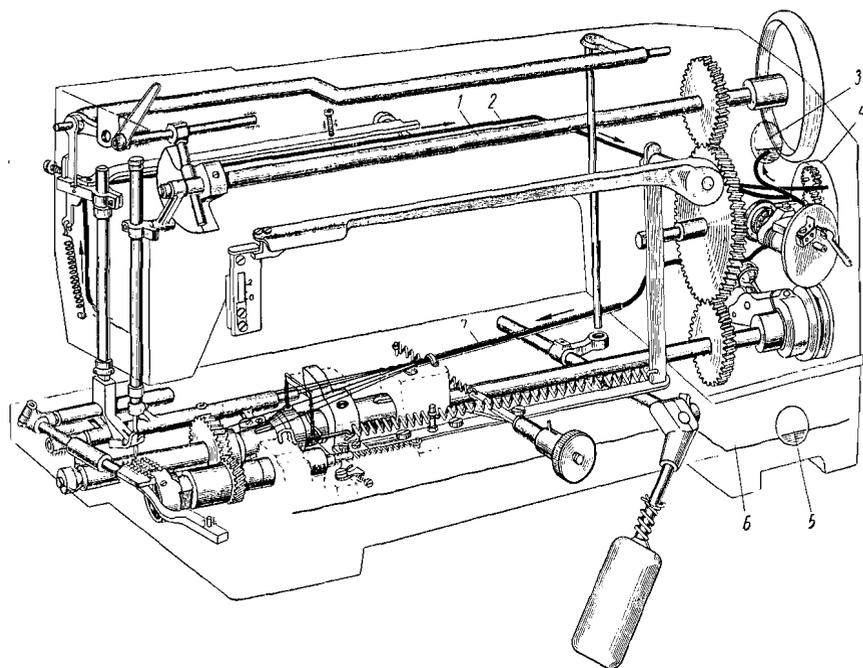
Схема смазки швейной машины 216-го класса «Сукра» Дюркопп
